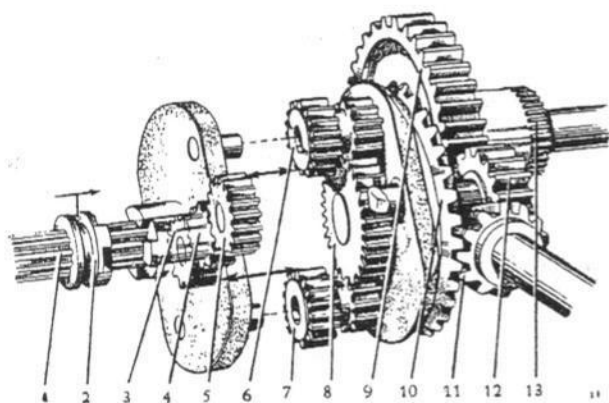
VUE DU DIFFÉRENTIEL ET DE LA COMMANDE DE ROUE, DÉGAGÉS DES CARTERS
